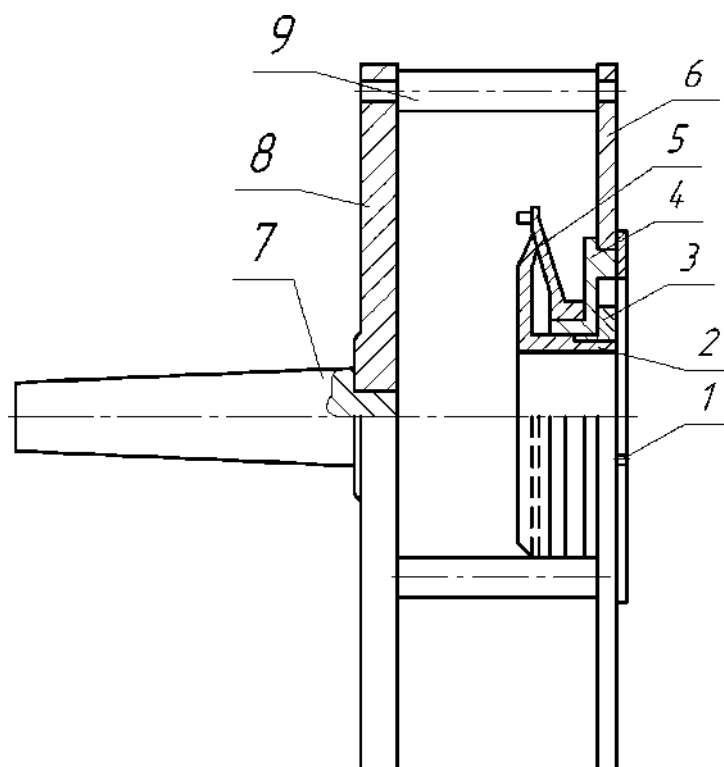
Схема пристосування для механічного оброблення підшипникових місць кришок генераторів: 1 – гайка; 2 – упор; 3 – дискова п'ята; 4 – перехідна втулка; 5 – змінна мембрана; 6, 8 – завзяті диски; 7 – настановний конус; 9 – розпірка
